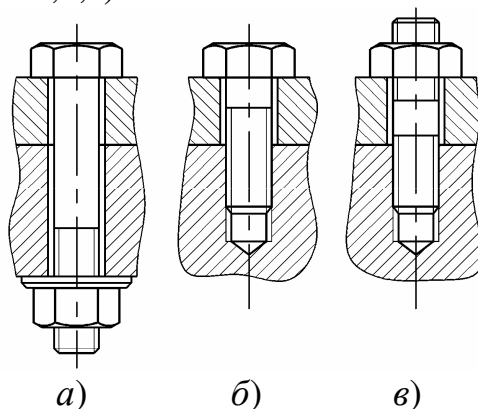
Виды резьбовых соединений: а) болтовое; б) винтовое; в) шпильчатое
